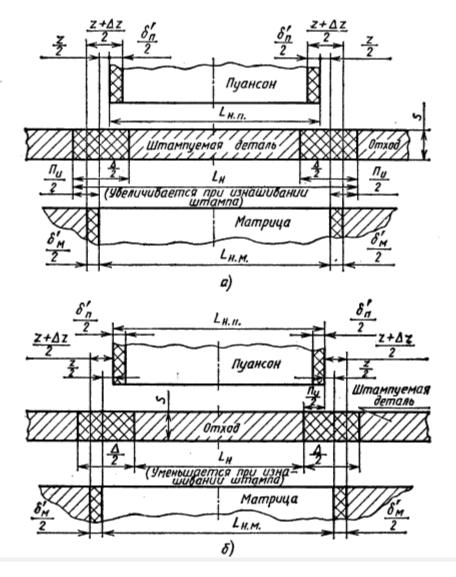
схема размеров и полей допусков штампуемого элемента и рабочих деталей штампа при их раздельном изготовлении: а- при вырубке; бпри пробивке
